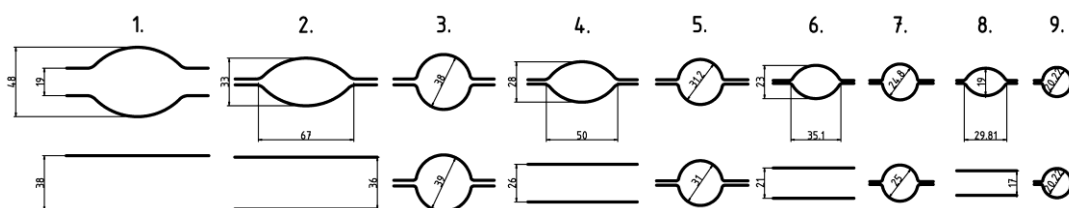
Калибровки для прокатки прутка по схемам «овал – круг» и «гладкая бочка – круг»
